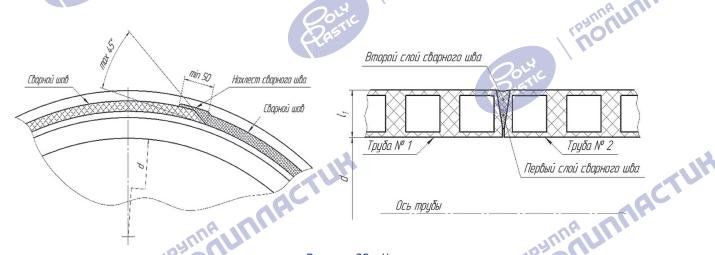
Схема наложения сварных швов при экструзионной сварке труб
